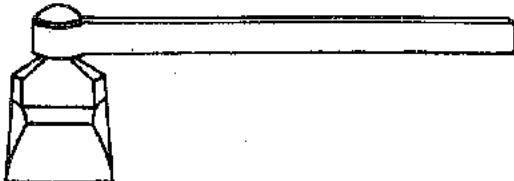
Soldador de martillo (Electric Materials Co.)
